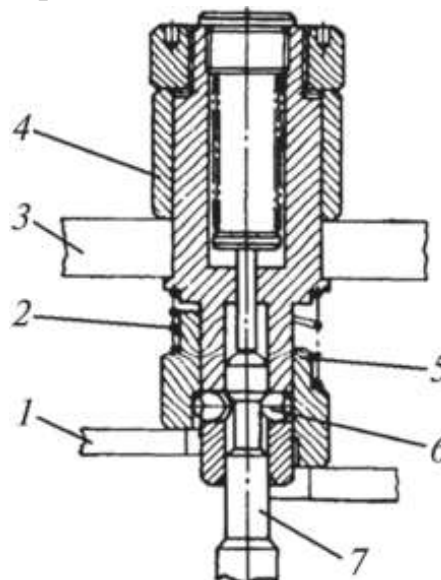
Схема допоміжного патрона вертикально-протяжного верстата
